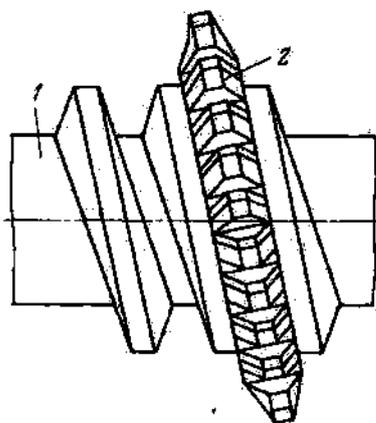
Схема нарезания червяков дисковыми фрезами: 1 - заготовка; 2 - инструмент
